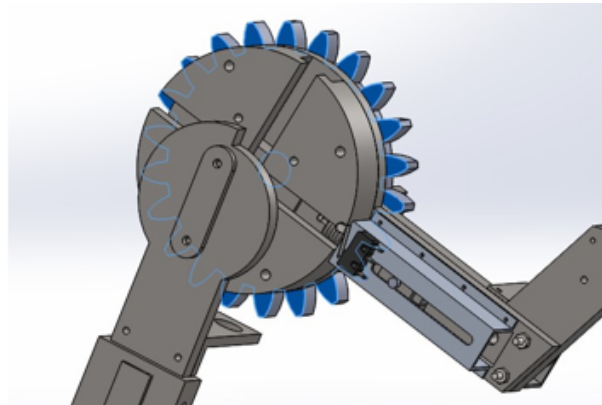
Engrenagem sobreposta à dupla-corrediça
